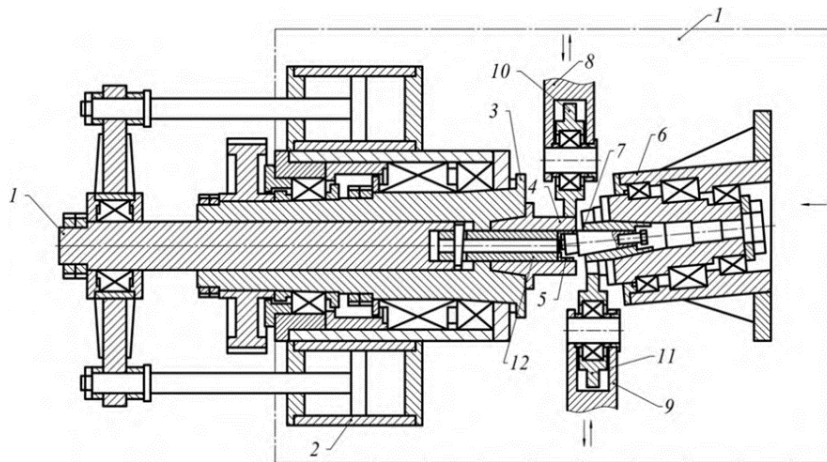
Обкочувальний інструментальний блок з конічним валком для виготовлення заготовок методом ШО: 1 – шток силового навантаження поздовжньої подачі заготовки; 2 – гідроциліндр; 3 – оправка обертального приводу матричного блоку; 4 – матриця; 5 – заготовка; 6 – блок валковий; 7 – валок конічний; 8, 10 – блок циліндричного валка радіального підпору матриці (заготовки); 9, 11 – блок циліндричного валка радіального підпору конічного валка, 12 – штовхач.
